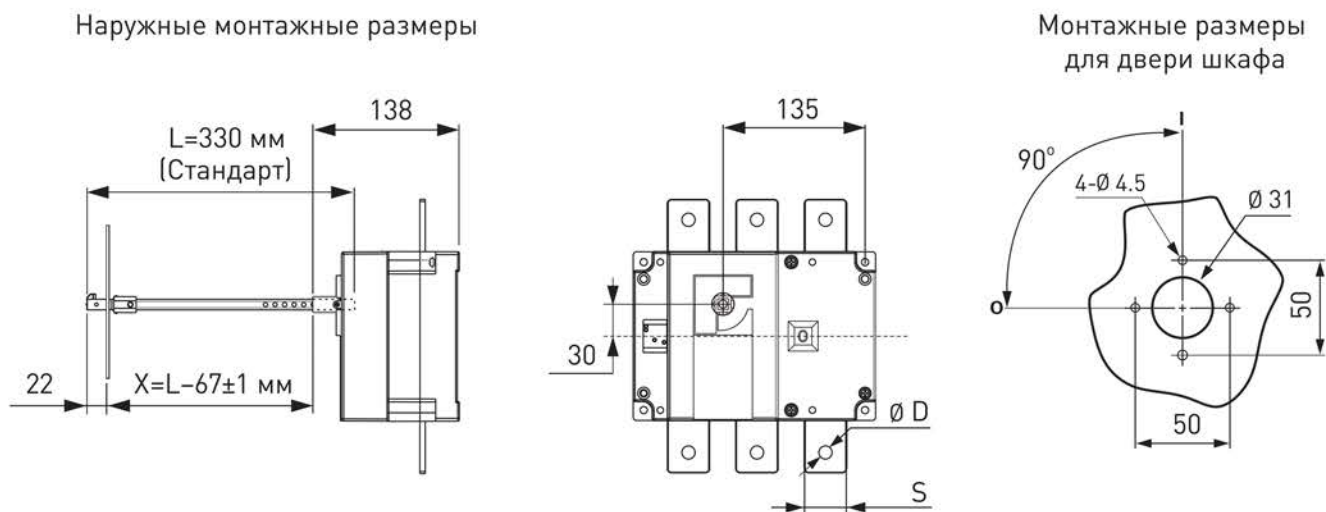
г – Монтажные размеры при установке на дверцу шкафа для рубильников 400-630 А
